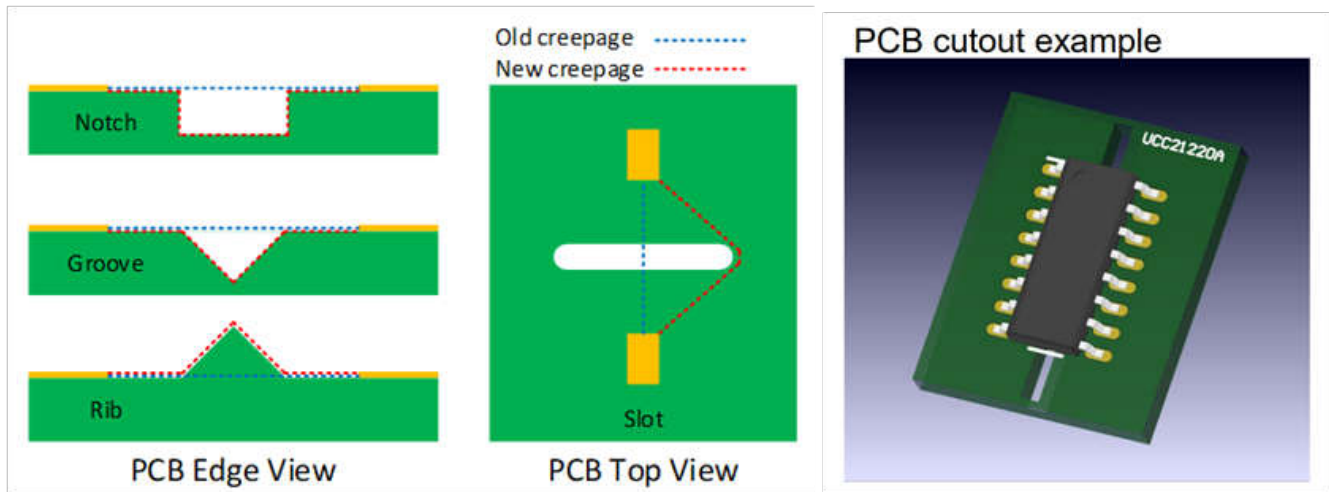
沿面距離を長くするための PCB のカットアウト方法
